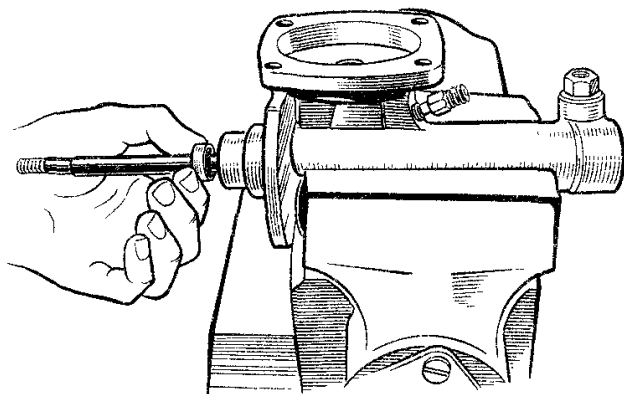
Установка первичной манжеты в корпус уплотнителей
